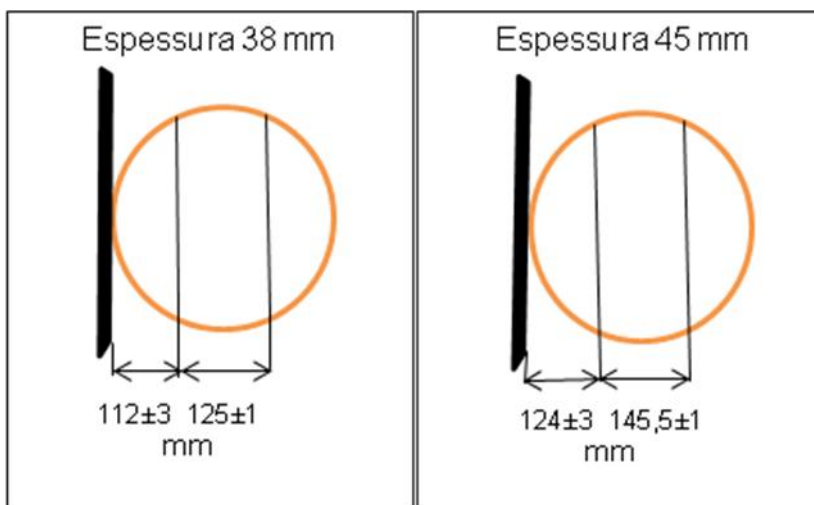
PLANO DE CORTE DA SERRA FITA TANDEM
